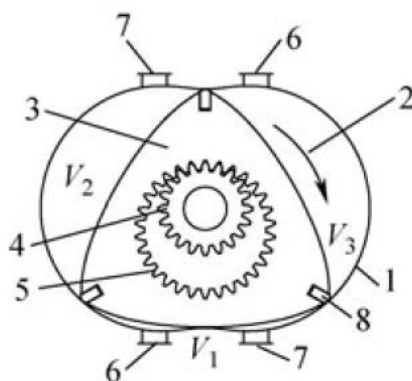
Схематичная диаграмма компрессора Ванкеля. 1. Цилиндр; 2. Камера; 3. Ротор; 4. Внешняя шестерня; 5. Внутренняя шестерня; 6. Впуск; 7. Выпуск; 8. Угловое уплотнение.
